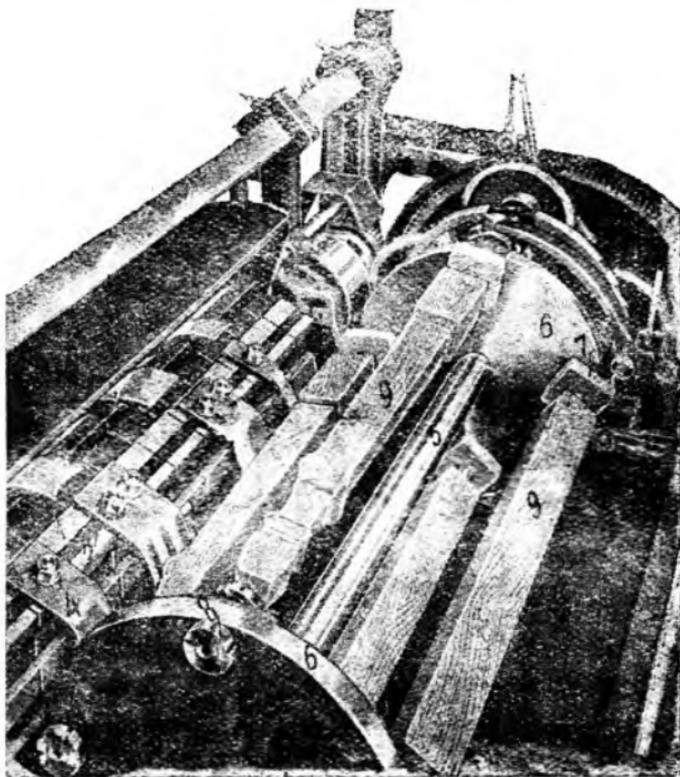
Ножевая головка и барабан карусельно-фрезерного токарного станка
